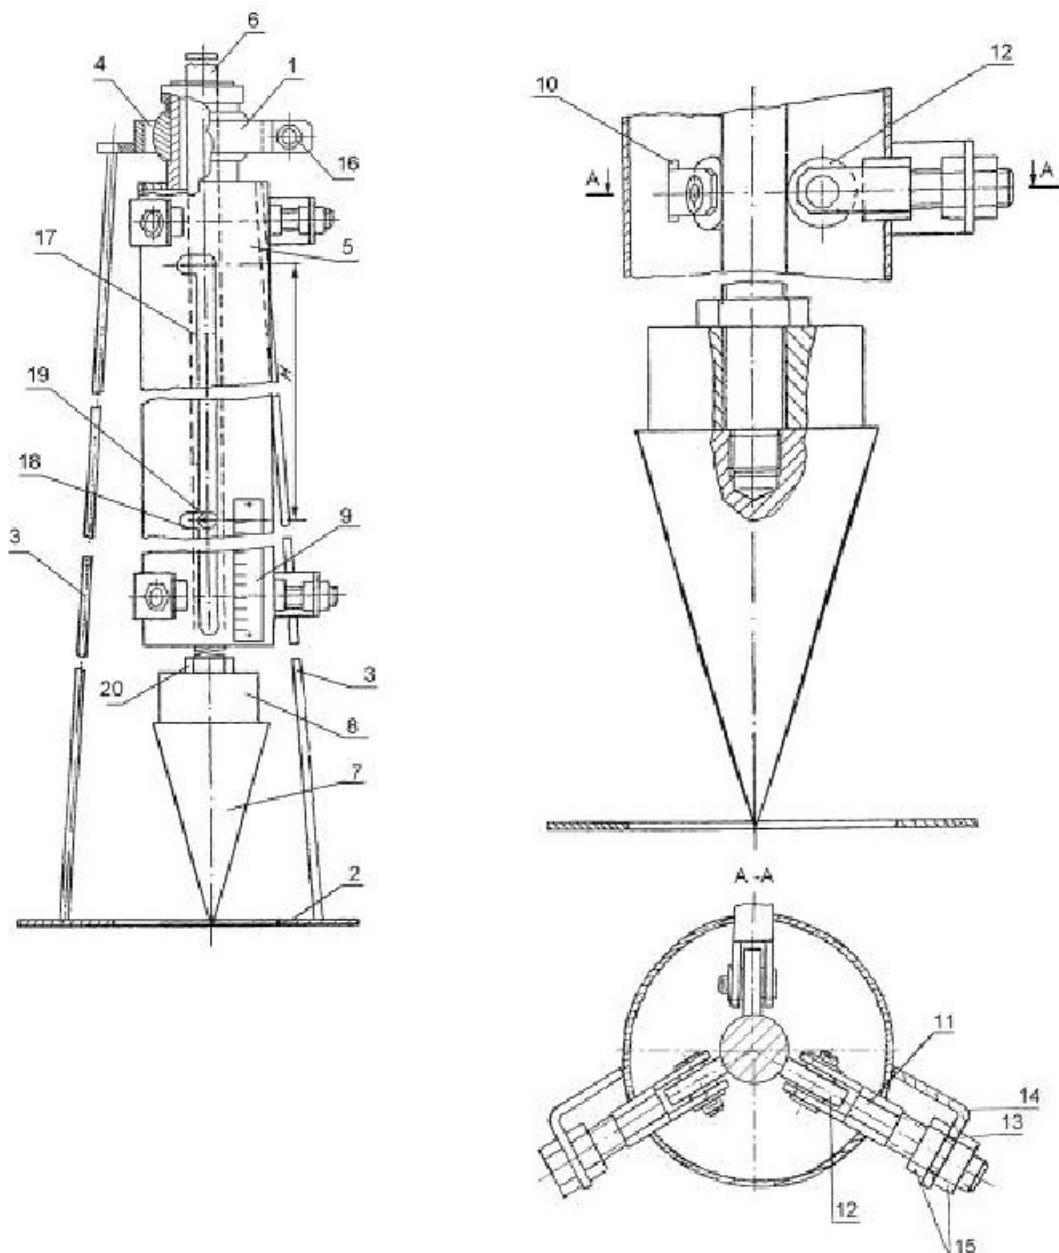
Конструктивное изображение стенда: 1 – корпус; 2 – основание; 3 – опоры; 4 – шаровый подшипник; 5 – направляющая труба; 6 – стержень; 7 – конический наконечник (индентор); 8 – сменный груз; 9 – мерная линейка; 10 – прямоугольное отверстие; 11 – вилка; 12 – подшипник качения; 13 – цилиндрическое отверстие; 14 – скоба; 15 – гайки регулировочные; 16 – гайка стопора; 17 – продольный паз; 18 – поперечный уступ; 19 – указатель со стрелкой; 20 – гайка.
